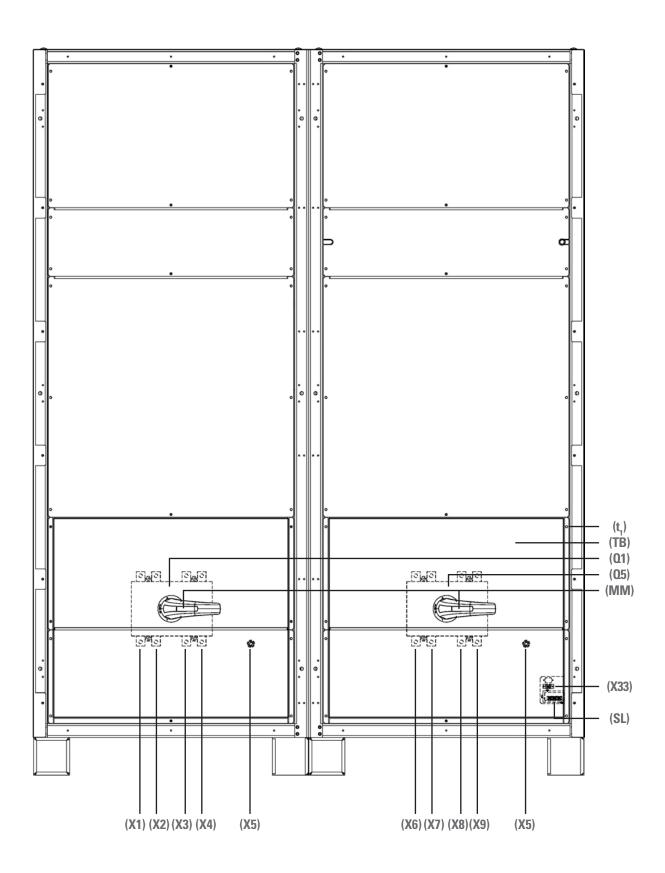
Vue frontale équipement triphasé en armoire avec des portes ouvertes, format n° 3.
